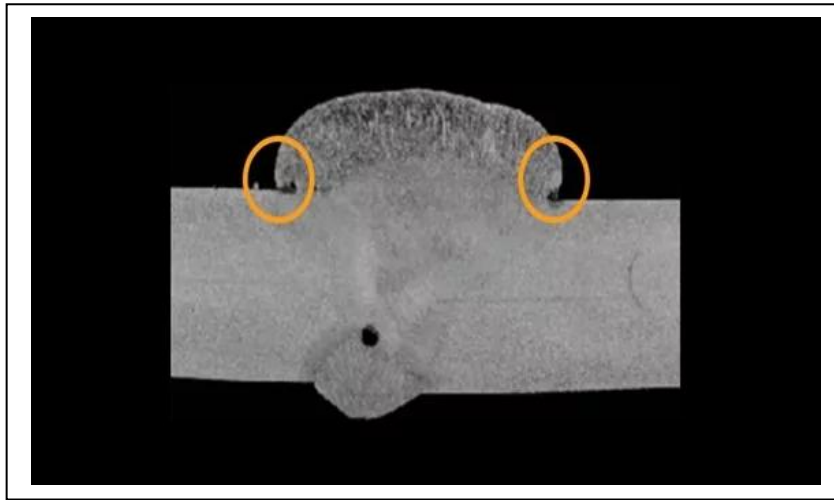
Cordon de soudure sous la forme d'un film discontinu. [33]
